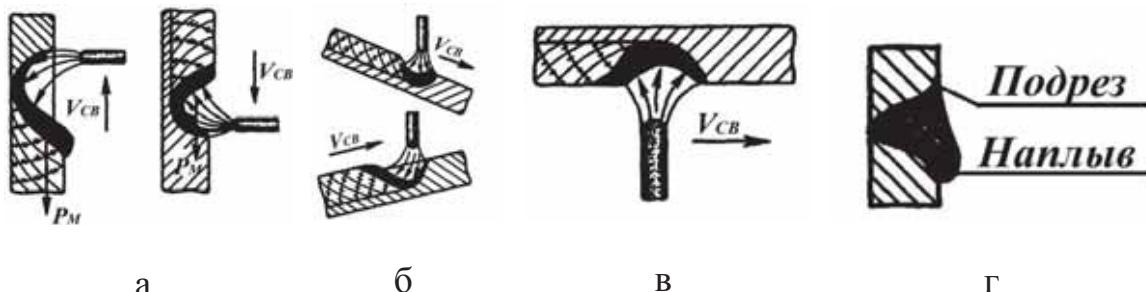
Формирование сварочной ванны в разных положениях:
